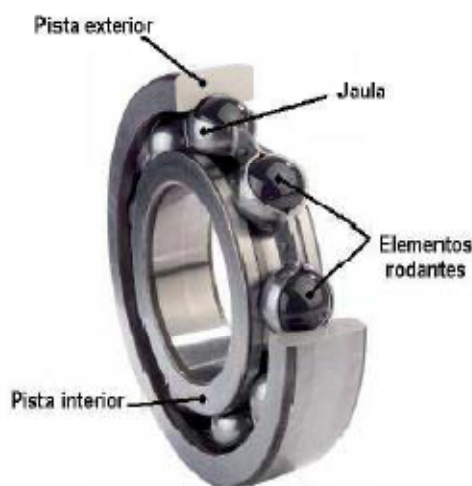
Esquema de las principales partes constitutivas de un rodamiento
